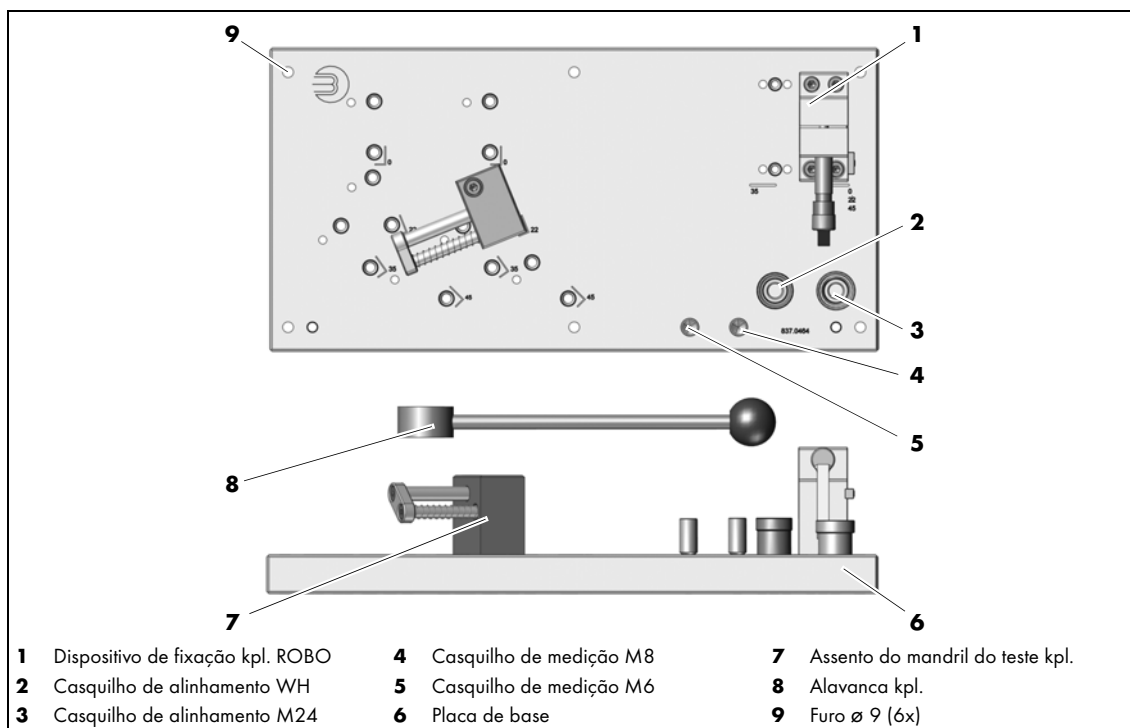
Instalar o dispositivo de ajuste VTS-Interlock
